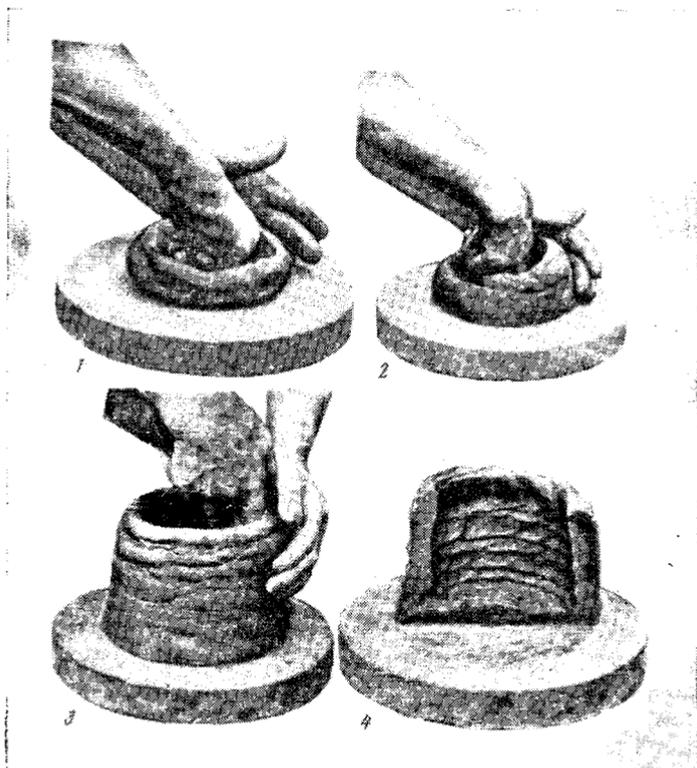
Основные этапы формовки наводом: 1 — «выбивание» днища; 2 — наводка первого жгута; 3 — наводка последнего жгута; 4 — общий вид заготовки сосуда (разрез)
